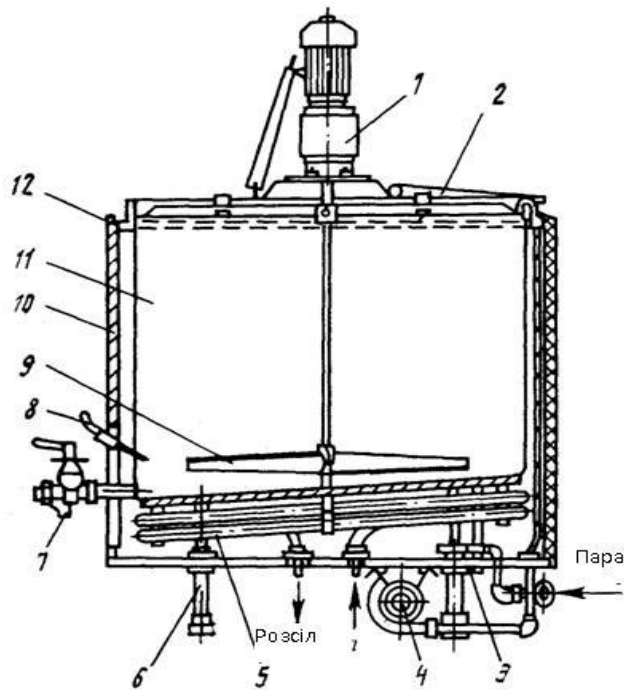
Резервуар універсального типу: 1 - привід мішалки; 2 - кришка; 3 - барботер; 4 - відцентровий насос; 5 - зміювик; 6 - ніжки; 7 - патрубок наповнення-спорожнювання; 8 - термометр опору; 9 - мішалки; 10 - зовнішній корпус; 11 - внутрішній корпус; 12 - пристрій, що зрошує.
